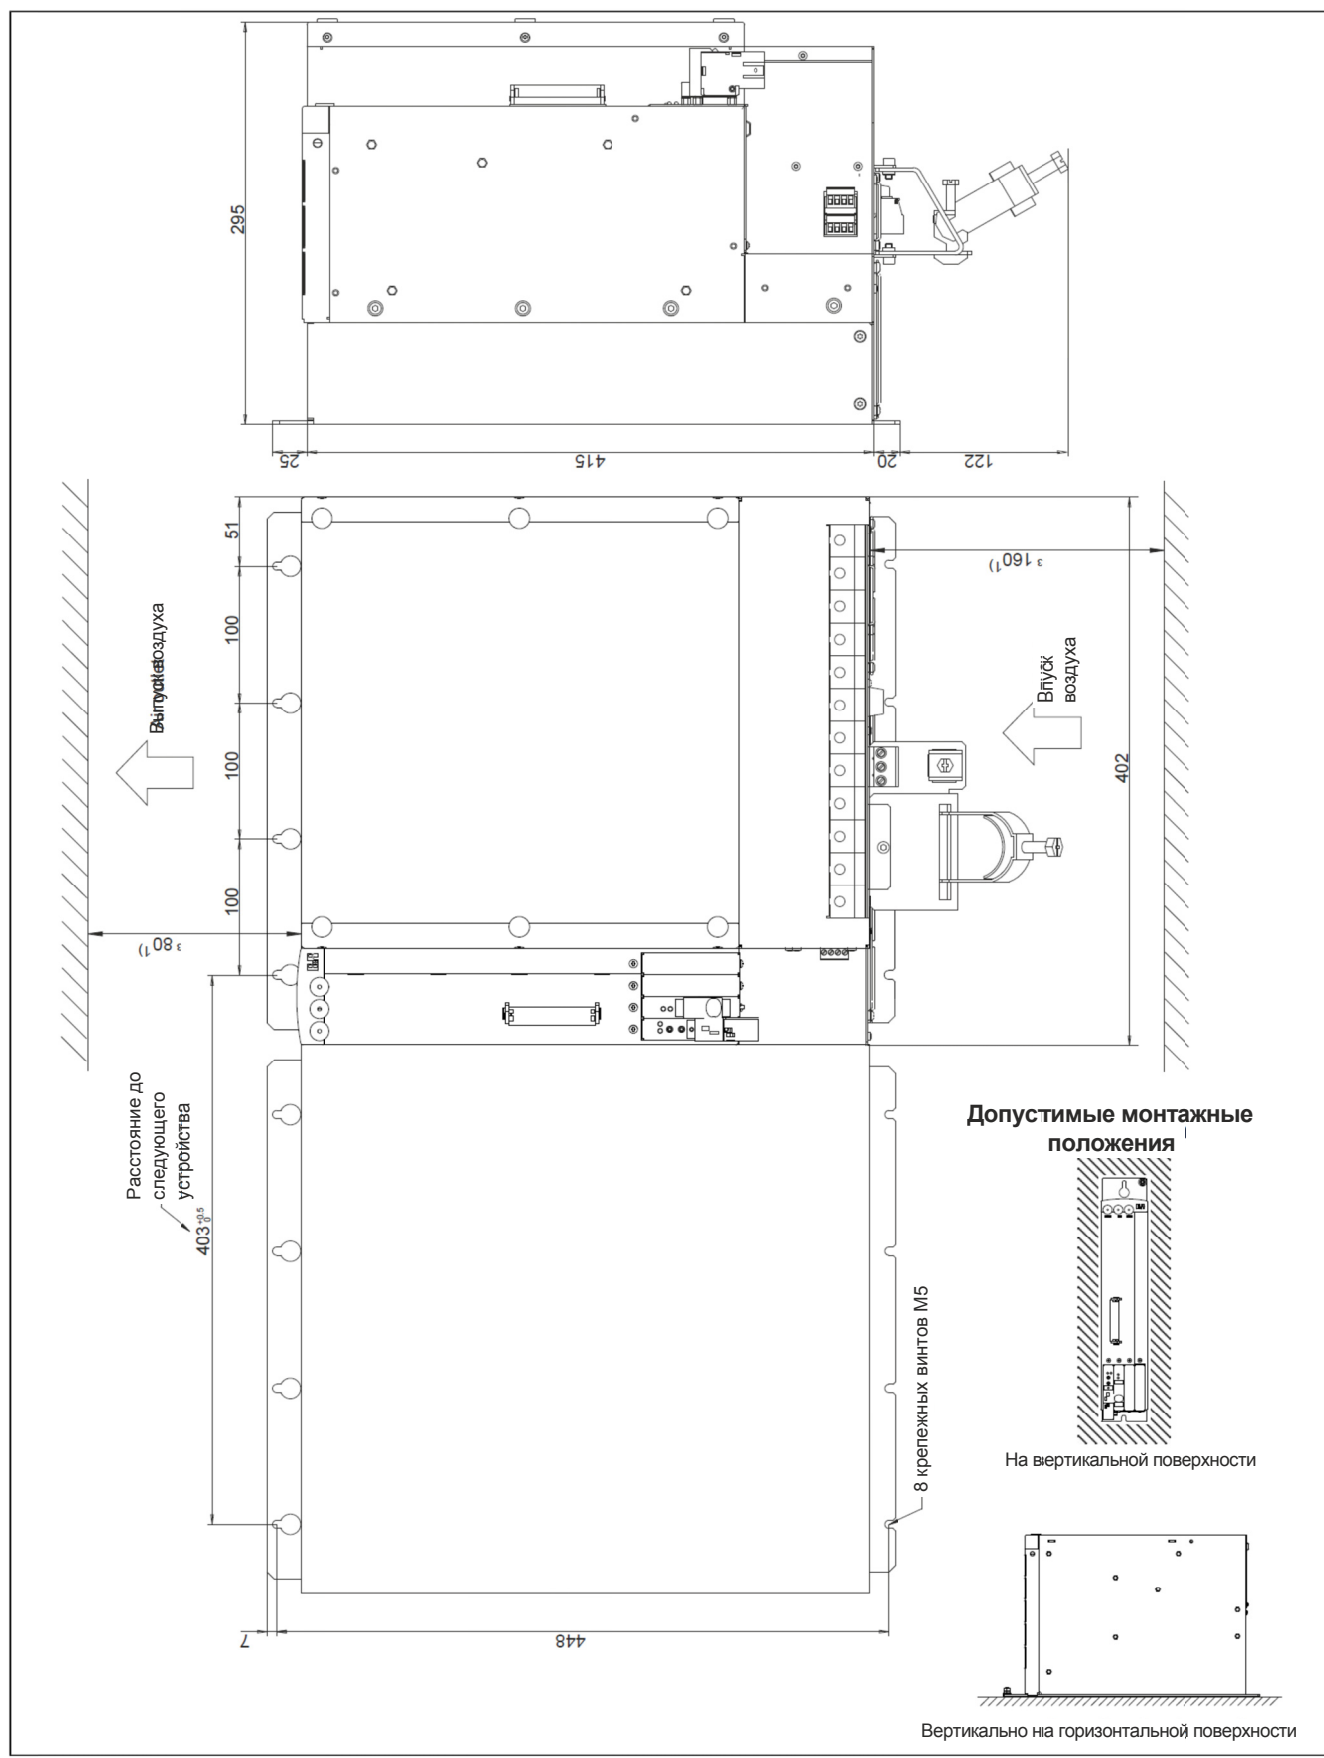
ACOPOS 128M – Габаритный чертеж и монтажные размеры
